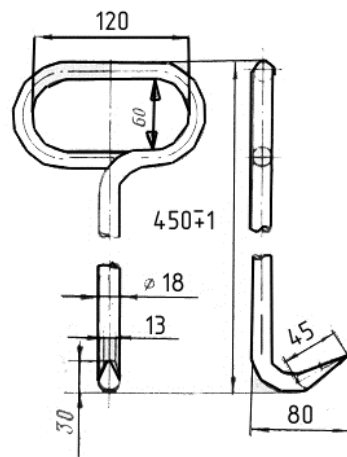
Крюк для открывания крышек колодцев пожарных гидрантов
